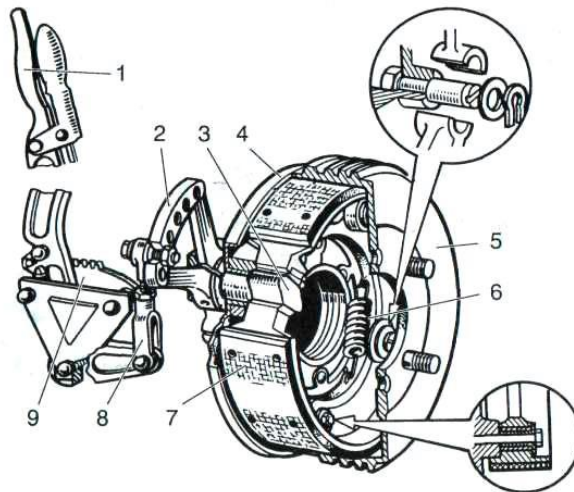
Схема механічного приводу стоянкової гальмової системи вантажного автомобіля: 1 – важіль з рукояткою; 2 – регулювальний важіль; 3 – розтискний кулак; 4 – опорний диск; 5 – гальмовий барабан; 6 – пружина; 7 – колодки; 8 – тяга; 9 – сектор.
